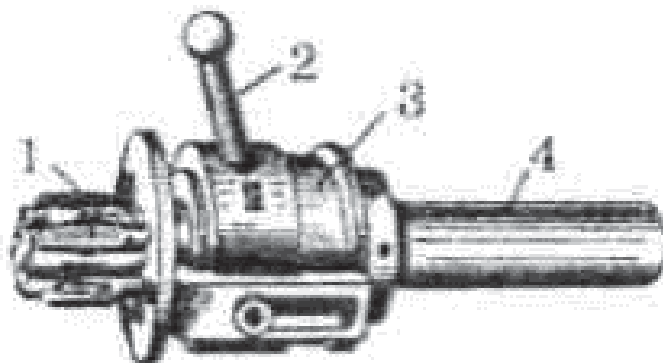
Резьбонарезная головка для нарезания внутренней резьбы:
